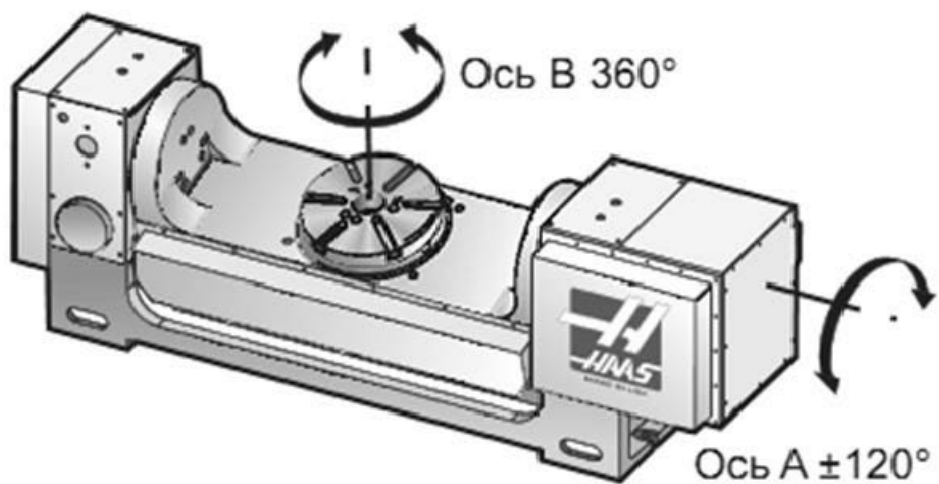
Наклонно-поворотный стол для делительного движения спутника на фрезерном станке с ЧПУ
